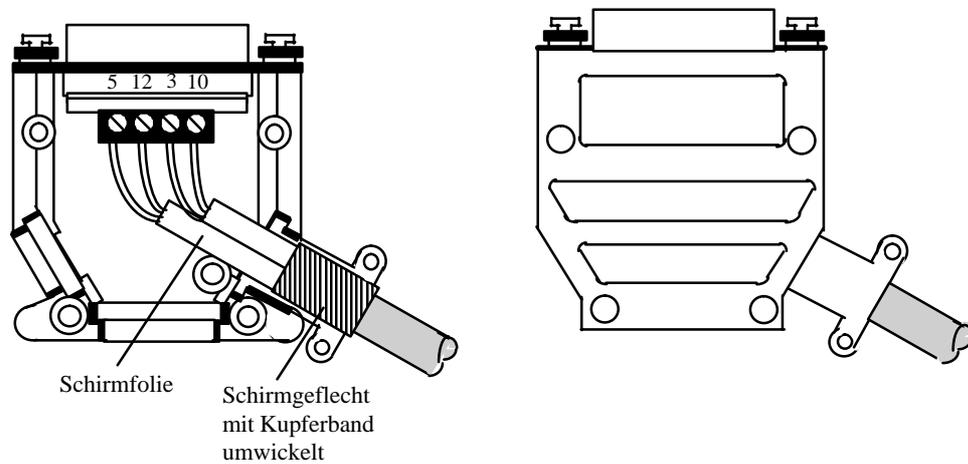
15-poliger Sub D-Stecker mit montierter Standardleitung
